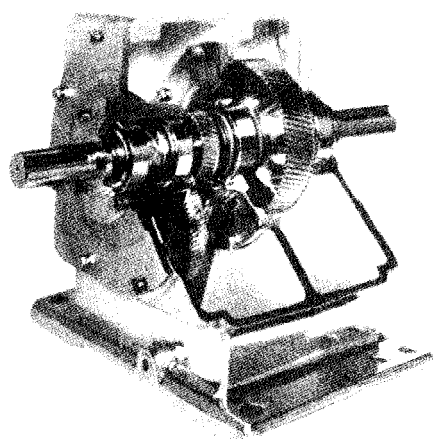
Reductor de engrane de reducción doble. Primera etapa, engranes helicoidales; segunda etapa, engranes de talla recta o cilíndricos. (Bison Gear & Engineering Corp., Downers Grove, Ill.)
